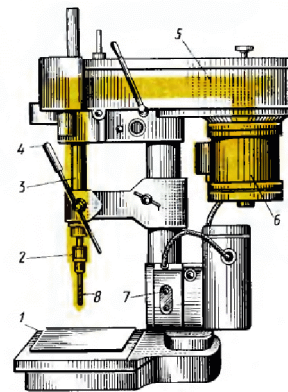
Настольный вертикально-сверлильный станок 2М112:
